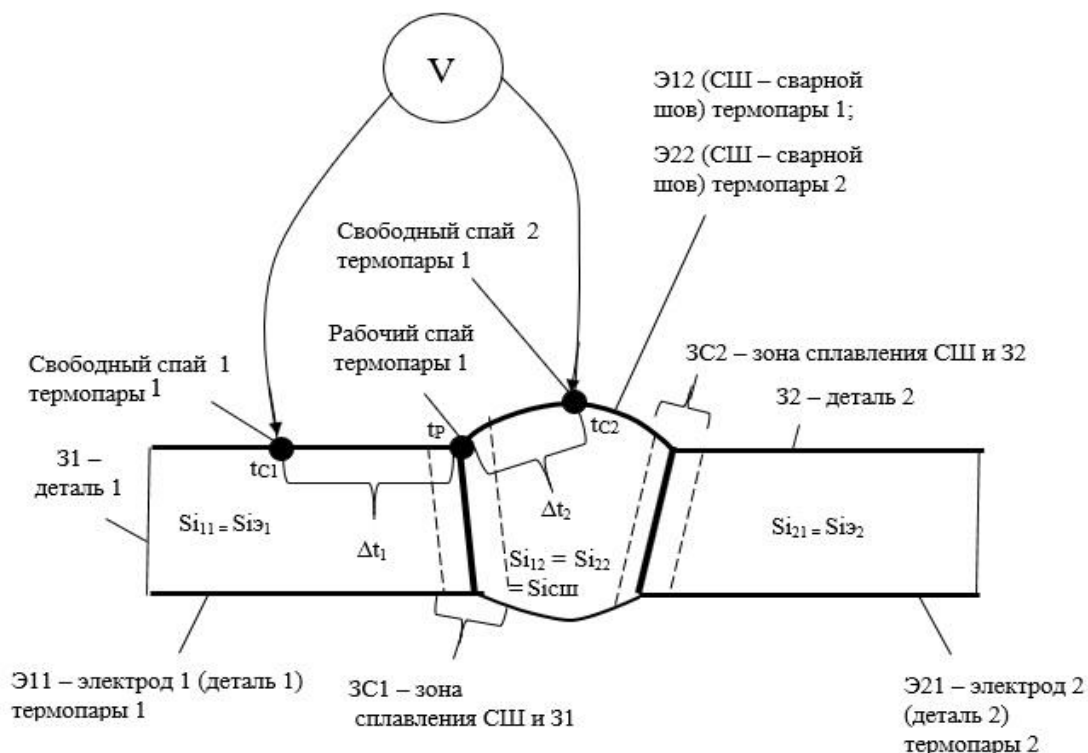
Схема открытого формирования ТЭДС с нагревом наружной стороны сварного соединения стальных обшивок судов поперёк шва
